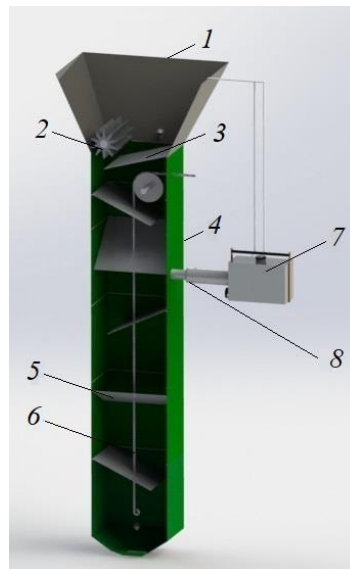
Схема пристрою для обробки насіння гарячим туманом: 1 – бункер для насіння; 2 – дозувальний апарат із приводним ребристим валиком; 3 – рухоме днище; 4 – камера обробки; 5 – похилі полиці; 6 – тросово-барабанний механізм; 7 – аерозольний генератор; 8 – сопло [2].
